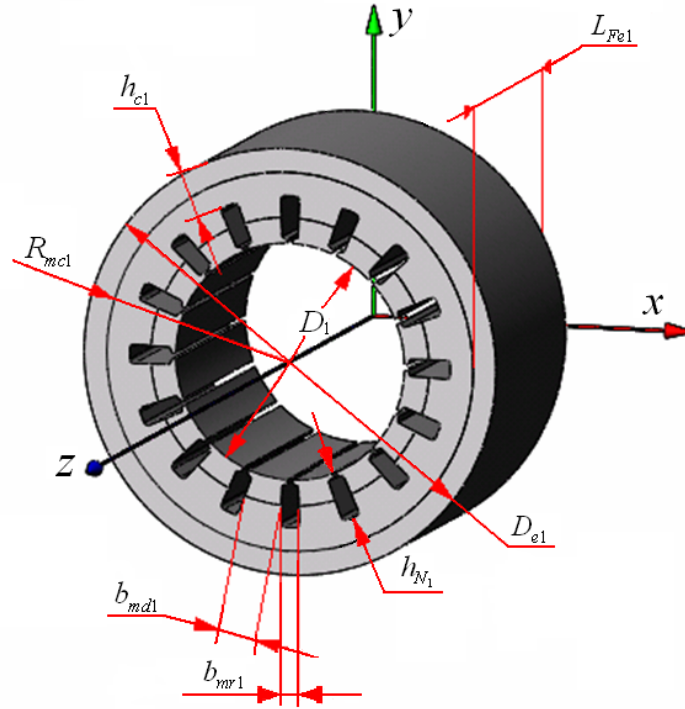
Dimensões geométricas do pacote de chapas do estator.
